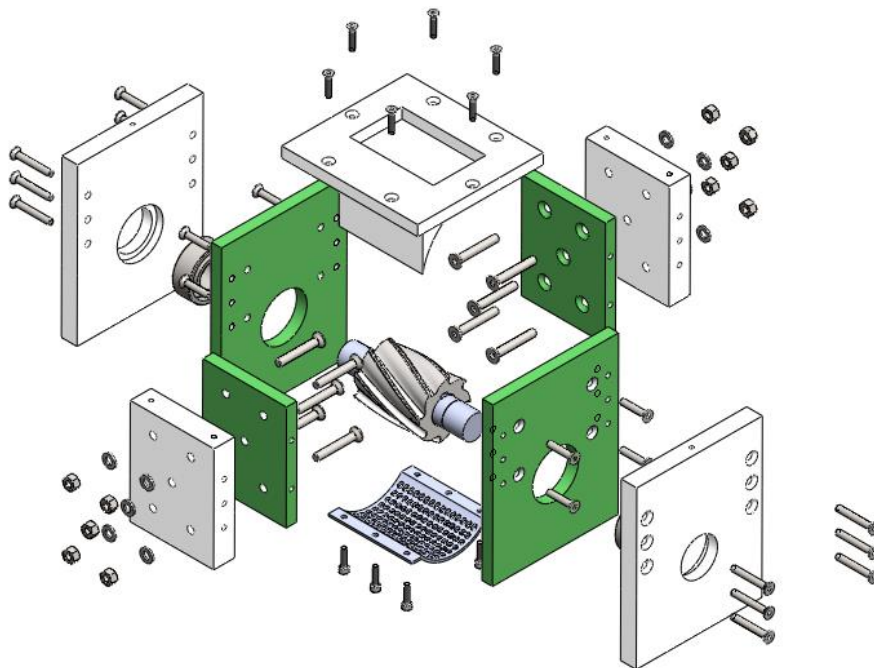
Conjunto explosionado (detalle Estructuras plástico) [Fuente propia]
